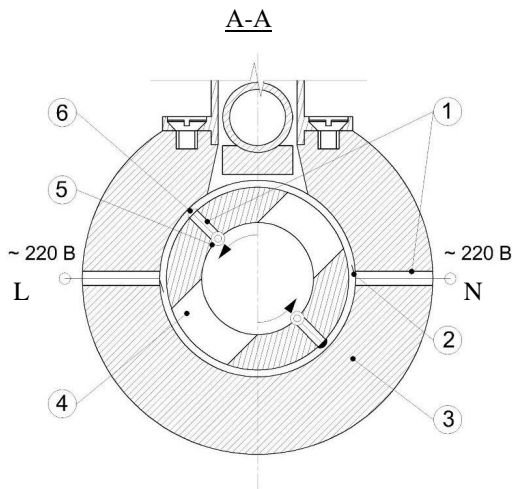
Розріз по А-А - система імпульсної подачі напруги для ініціювання зарядів вибухової речовини на вибій: 1 – канали з електродами; 2 – пластина контактна; 3 - корпус вертлюга модифікованого; 4 – вал вертлюга; 5 –
